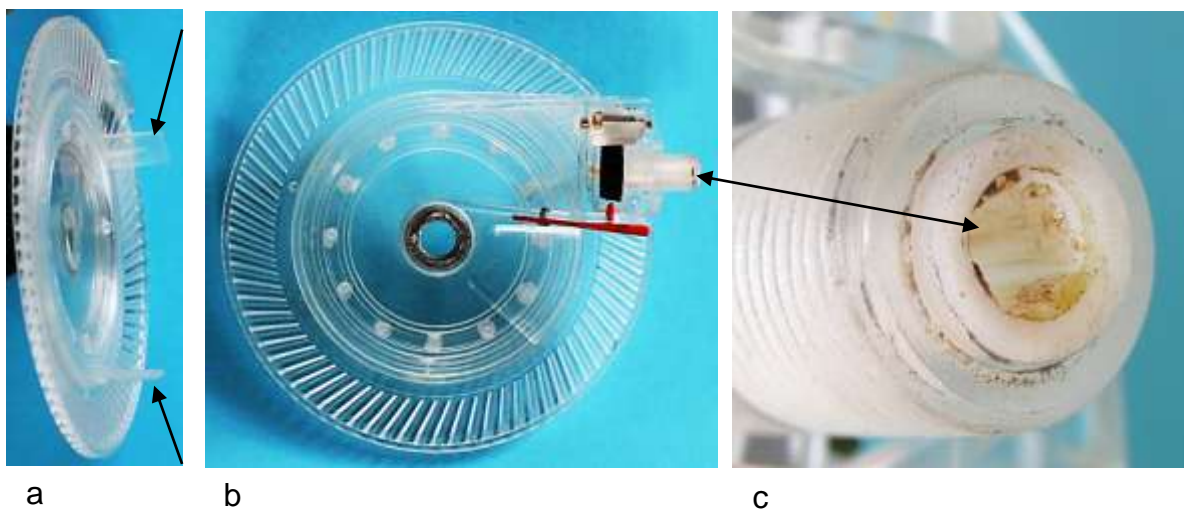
Winkelgetriebestufe: a) Ansicht der Mitnehmer, b) Schrägverzahntes Zahnrad, c) Kupplung mit Innenvierkant für die biegsame Welle
